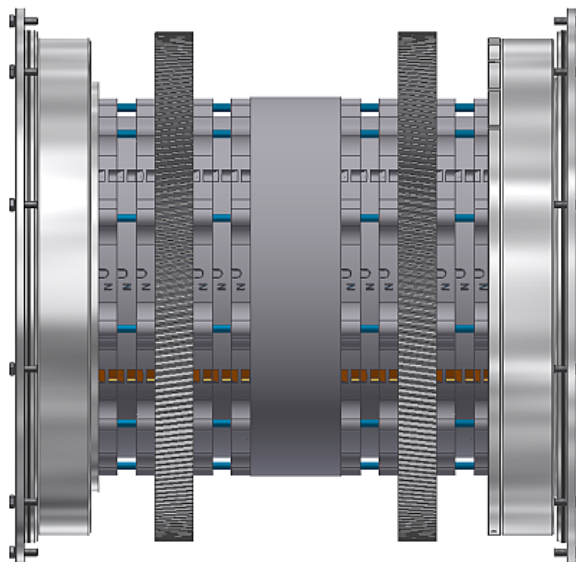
Magnettrommel aus zwei gekoppelten Segmenten mit Zahnradscheiben und Schrägkugellagern
